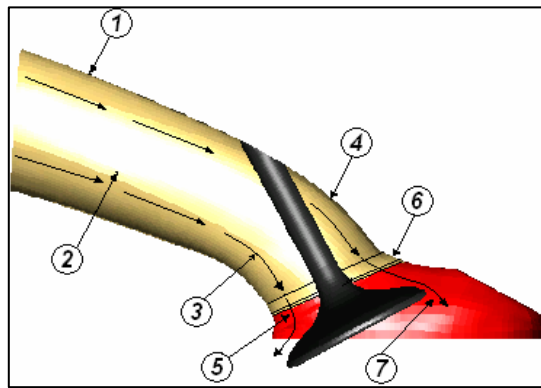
Partes críticas del conjunto ducto – válvula de admisión
